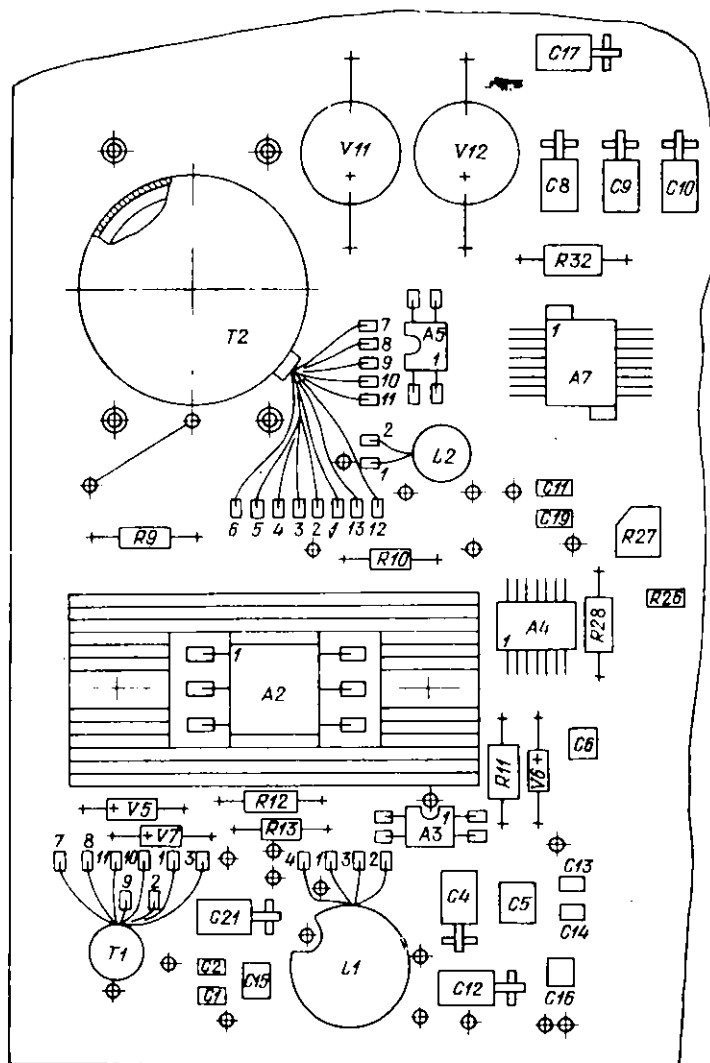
Фрагмент сборочного чертежа ИВЭ:
